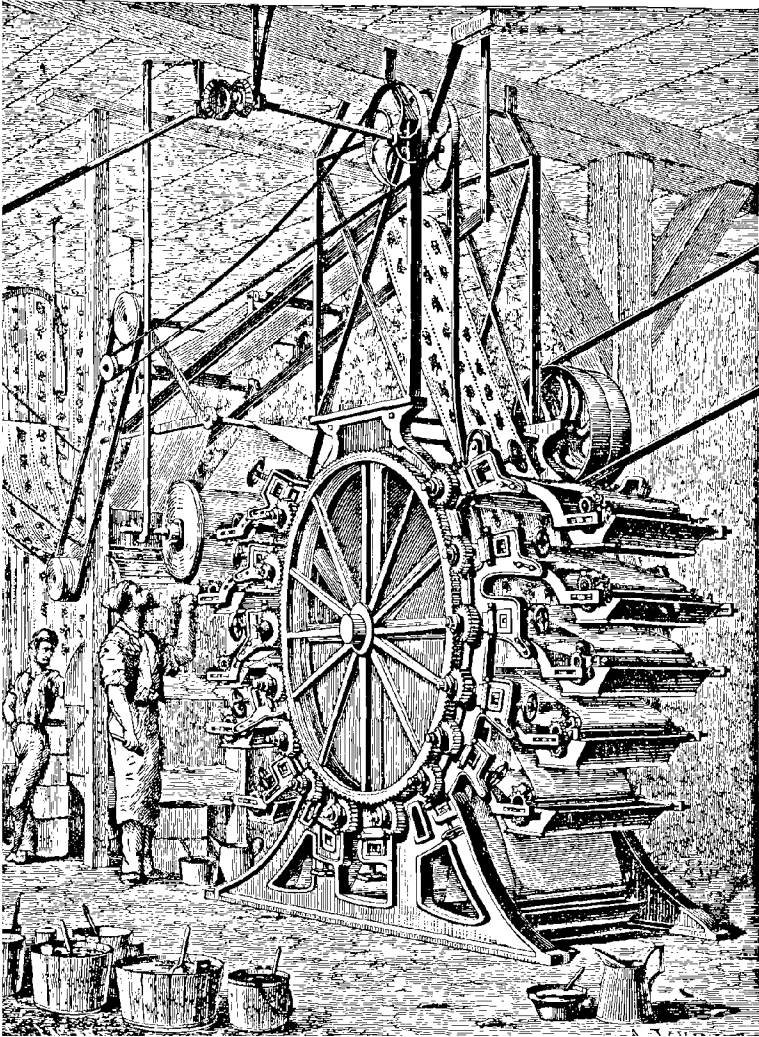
Machine pour imprimer les papiers peints en dix couleurs.
